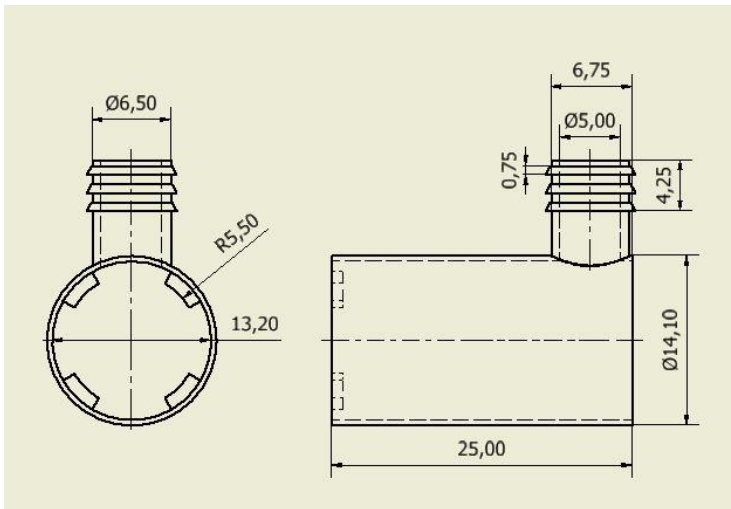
Tampak luar *greaser shell* hasil *redesign* yang telah di *assemble* dengan *spindle gear
